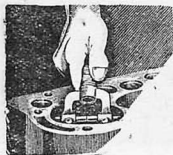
Установка микрометрического нутрометра внутрь цилиндра
